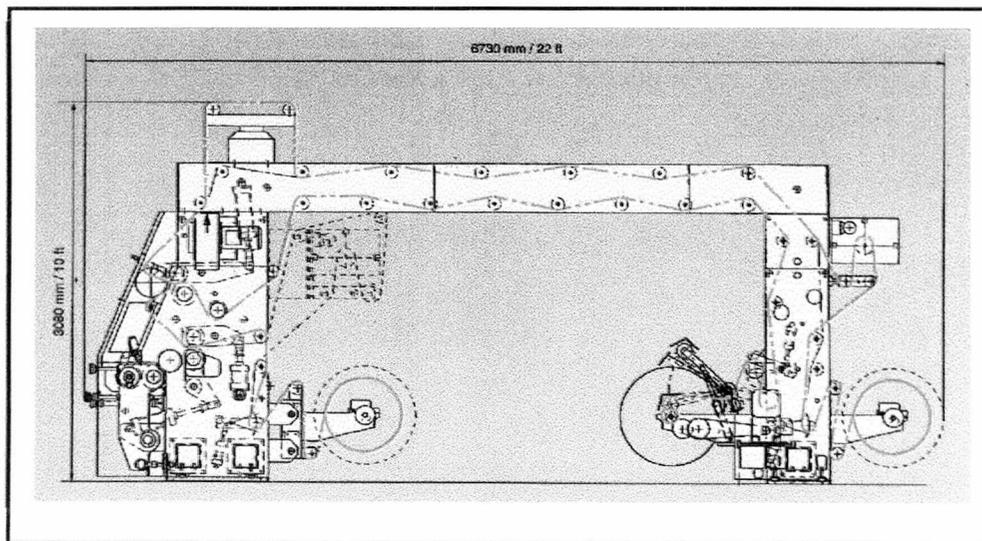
Máquina de corte e solda *Stand-up pouch*.
